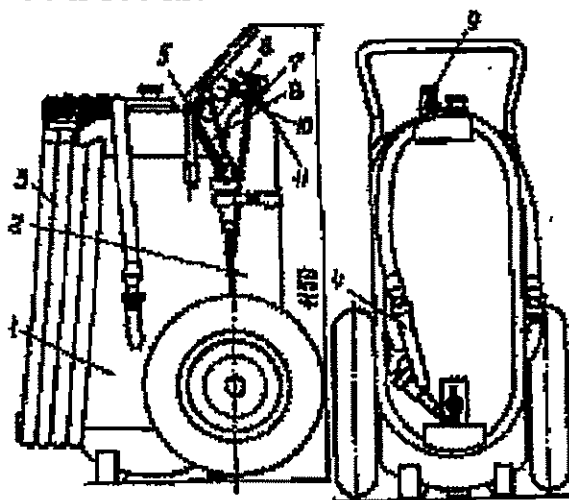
Общий вид передвижного порошкового огнетушителя ОП-100:
